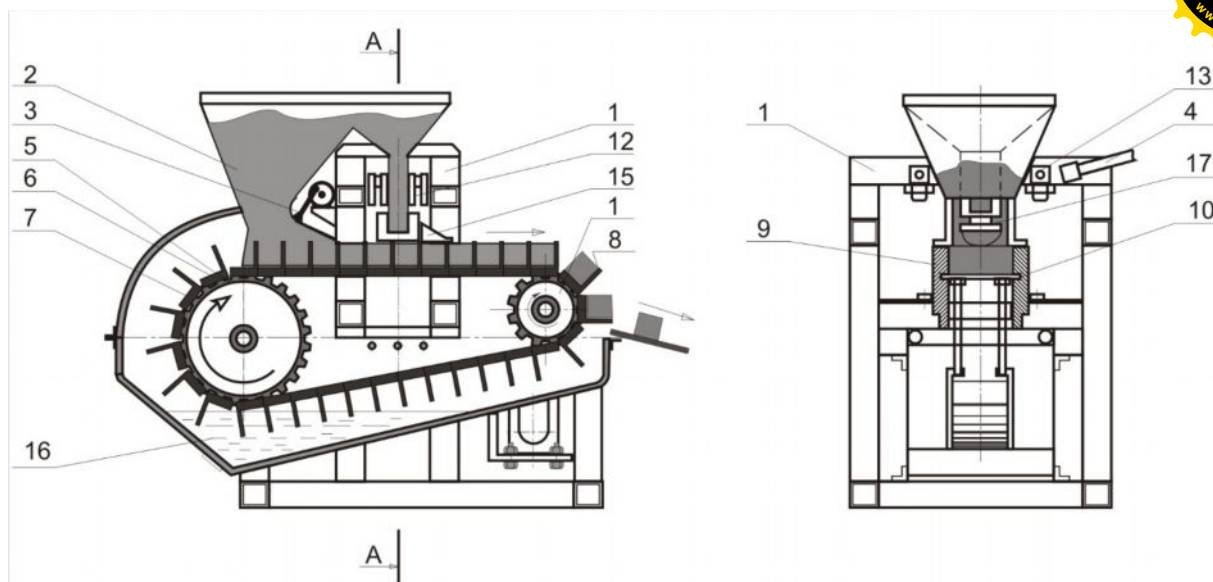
Конструктивная схема; а) общий вид прессового оборудования; б):
